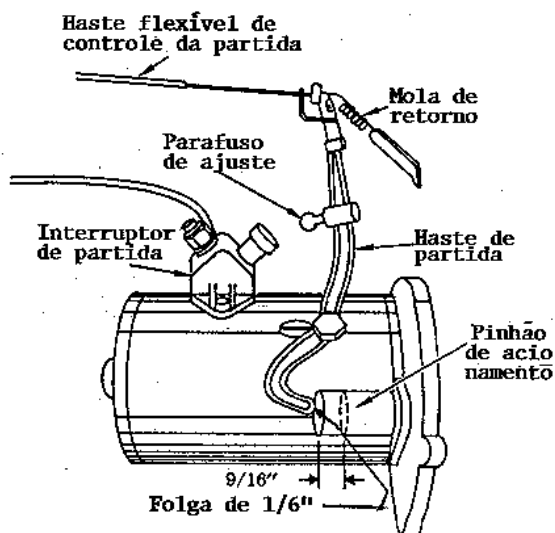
Hastes de controle do motor de partida e ajustes.
